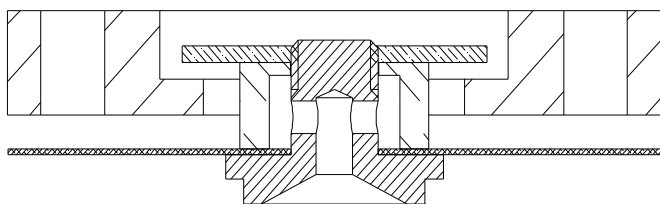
"СБОРКА ДЕТАЛЕЙ (38), (39) И (41)"
